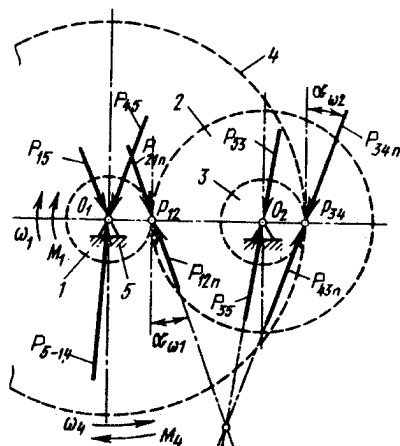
Кинематическая схема двухступенчатого зубчатого редуктора
